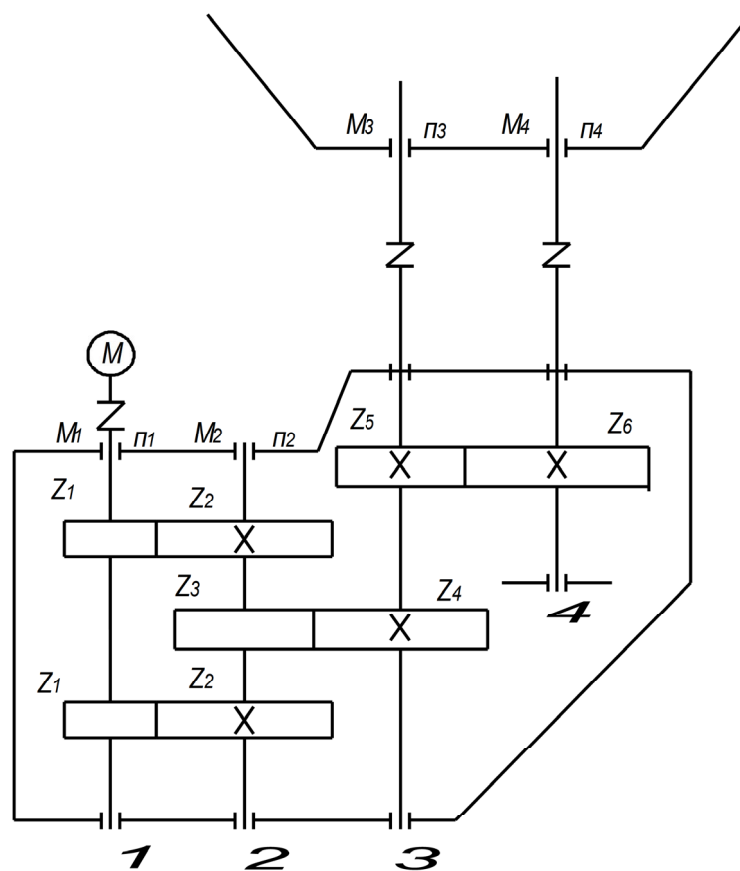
Розрахункова схема редуктора приводу роторів змішувальної машини
